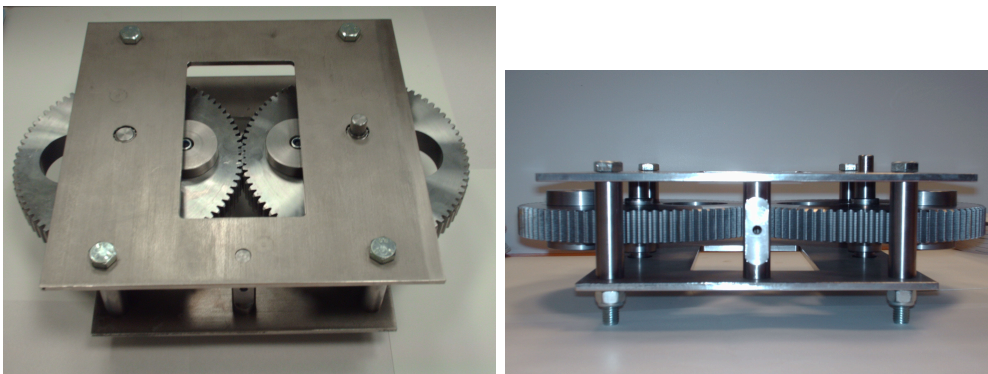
Excitador mecánico rotativo. Izquierda: Planta. Derecha: Alzado.
